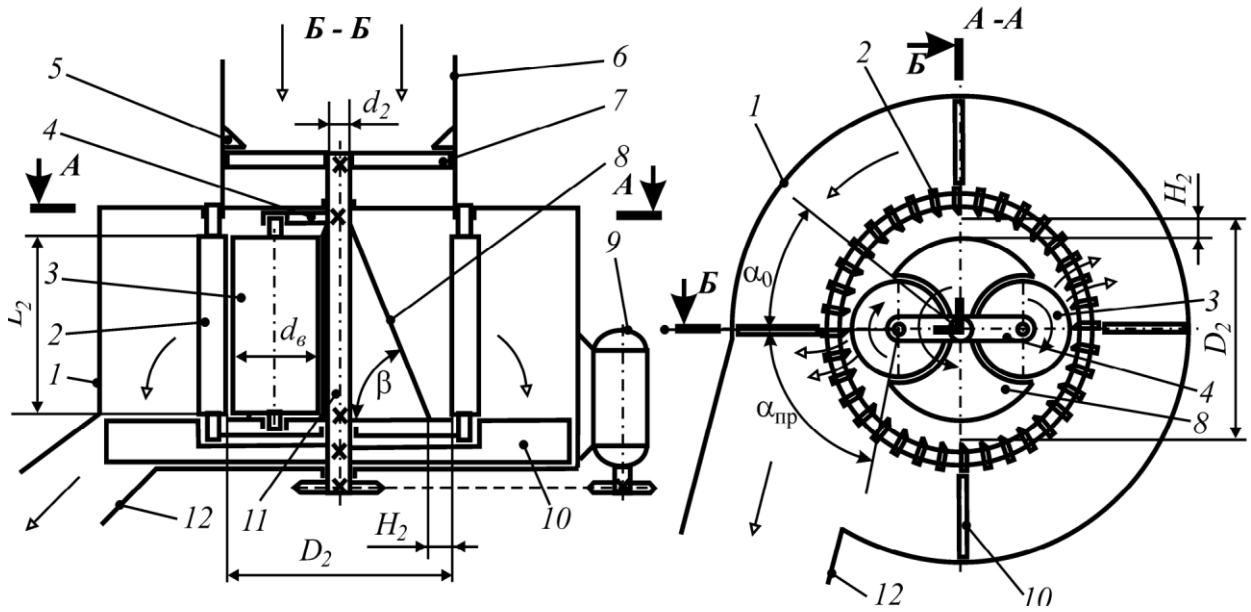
Схема для визначення конструктивних параметрів другого ступеня подрібнення: 1 – кожух; 2 – ніж пластинчастий; 3 – валець; 4 – напрямні; 5 – протирізі; 6 - завантажувальна горловина; 7 – ніж горизонтальний; 8 – конус; 9 – привід; 10 - крильчатка; 11 - вал другого ступеня подрібнення; 12 – вивантажувальний лоток
